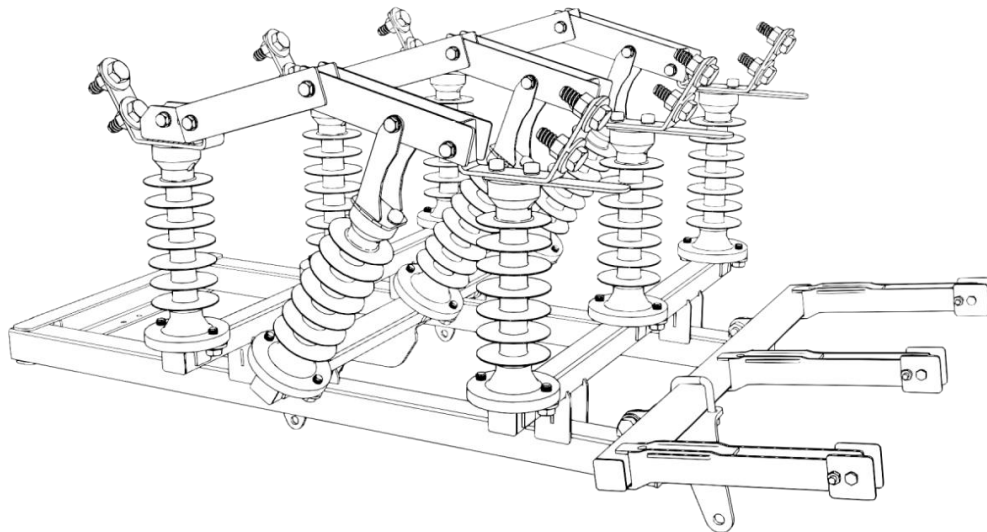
а Конструкция разъединителя с заземлителем с одной стороны
